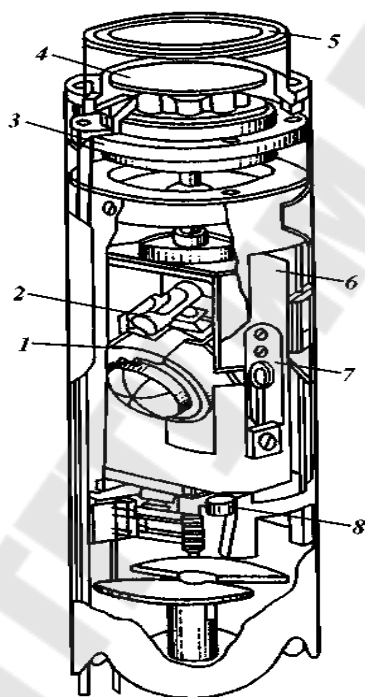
Гироскоп в глубинном инструменте многократного действия: 1 – сборка мотора для гироскопа; 2 – нивелирующий переключатель; 3 – сборка вращающего мотора; 4 – гирокарта; 5 – шкала верньера; 6 – внешний шарнир; 7 – внутренняя опора шарнира; 8 – нижняя внешняя опора шарнира
